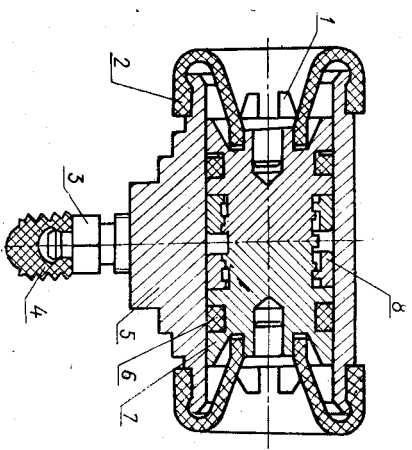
Колесный тормозной цилиндр с устройствами для автоматической регулировки зазоров между колодками и барабаном:
